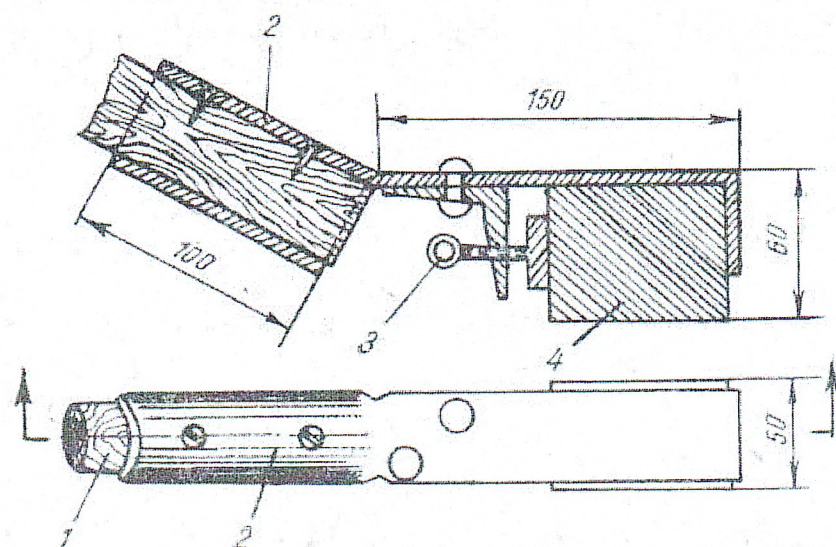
Ramă metalică pentru fixarea pietrei de șlefuit: 1 — miner; 2 — ramă metalică; 3 — șurub de fixare; 4 — placă de șlefuit.
